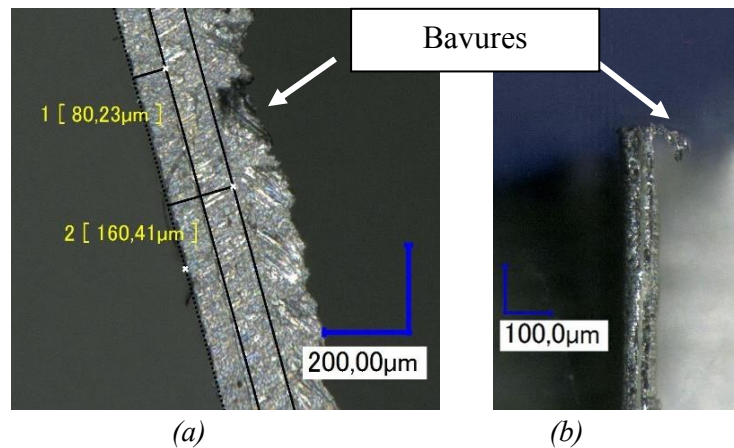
Bavures au niveau des parois doubles : (a) vue de face ; (b) vue de coupe.
